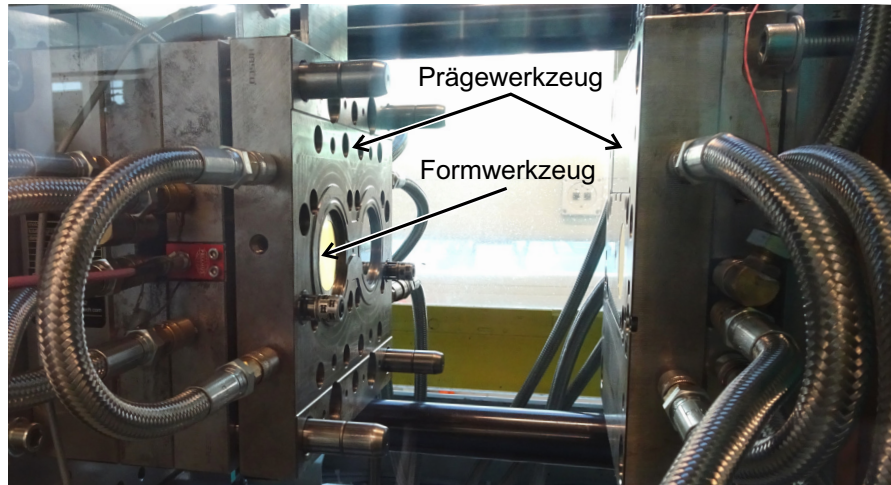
Prägewerkzeug am INKA mit eingesetztem Formwerkzeug aus Messing (links). Der linke Teil des Prägewerkzeugs wird beim Spritzprägen gegen den rechten Teil gepresst, während das PMMA von rechts eingespritzt wird.
